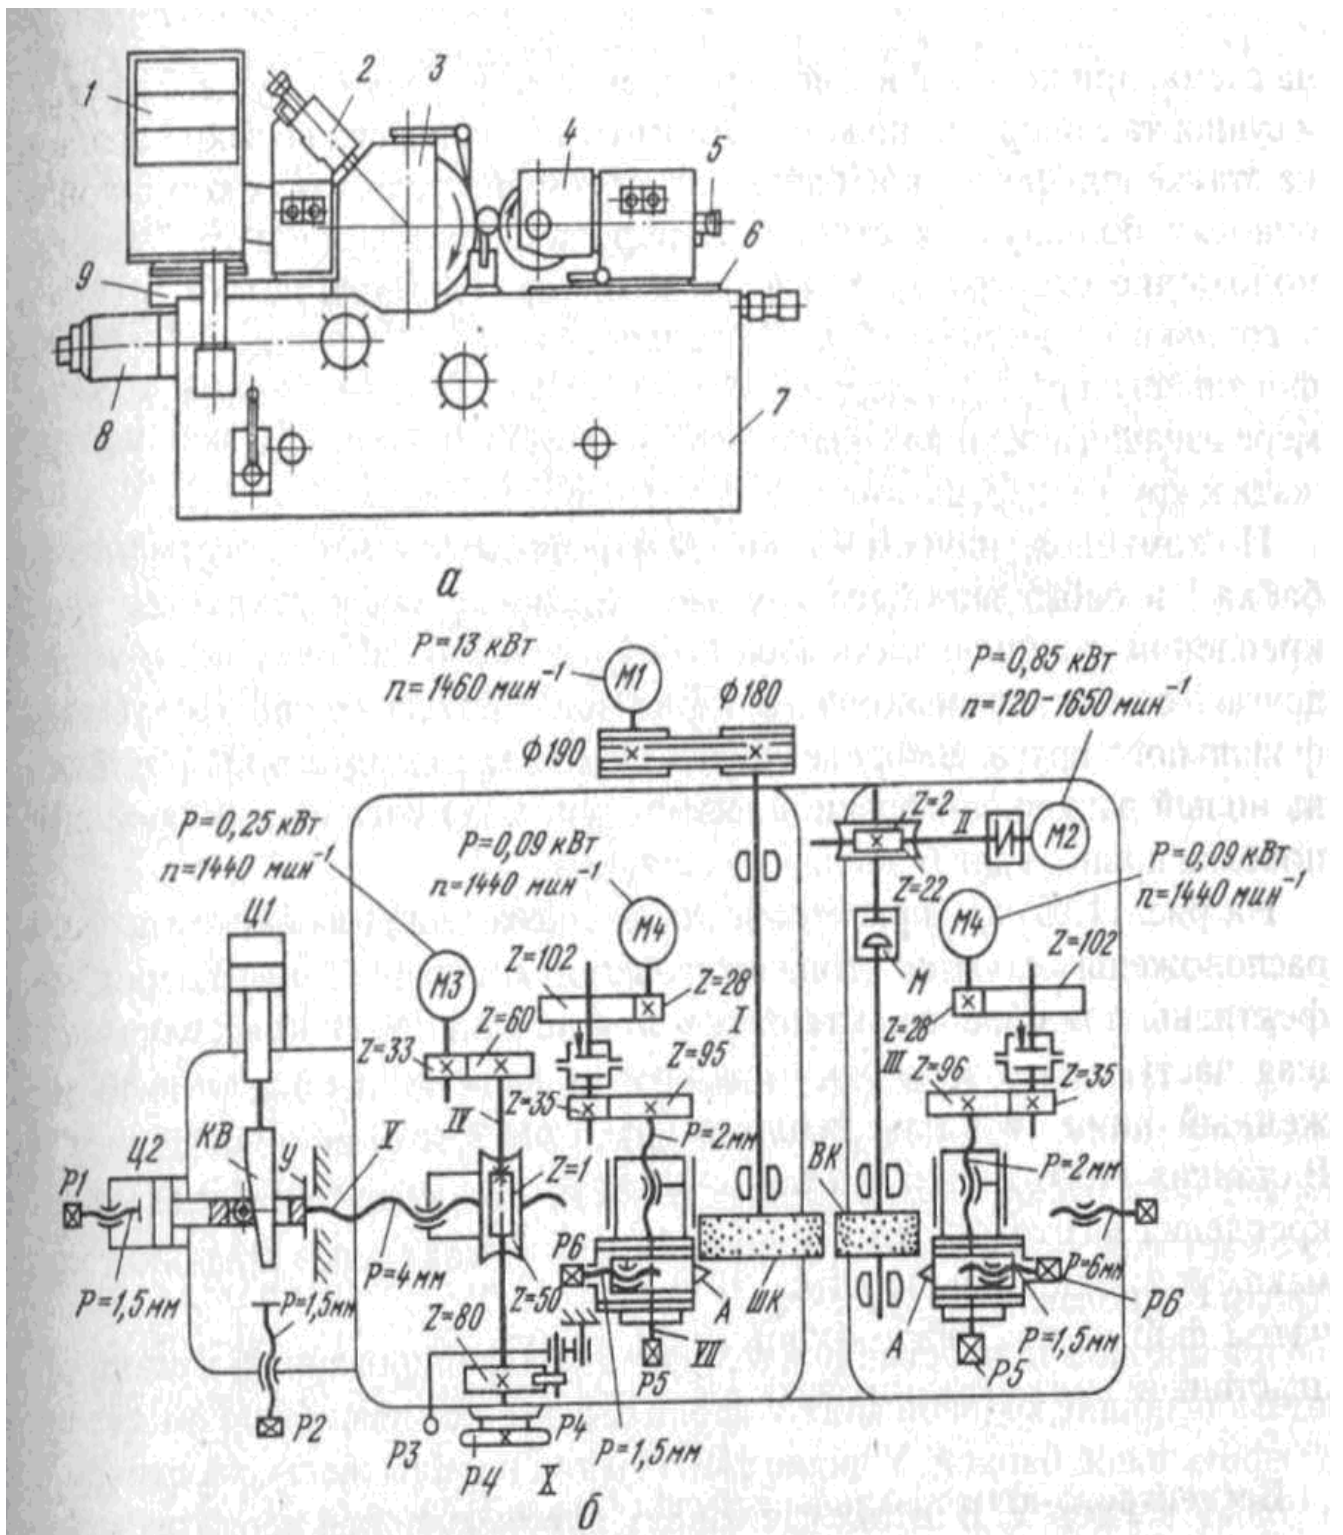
Бесцентровый станок для наружного круглого шлифования модели 3М184: а – компоновка: 1 – блок управления, 2, 5 – приспособления правки шлифовального и ведущего кругов, 3 – шлифовальная бабка, 4 – бабка ведущего круга, 6 – салазки бабки ведущего круга, 7 – станина станка, 8 – устройство подачи на врезание, 9 – салазки шлифовальной бабки;
